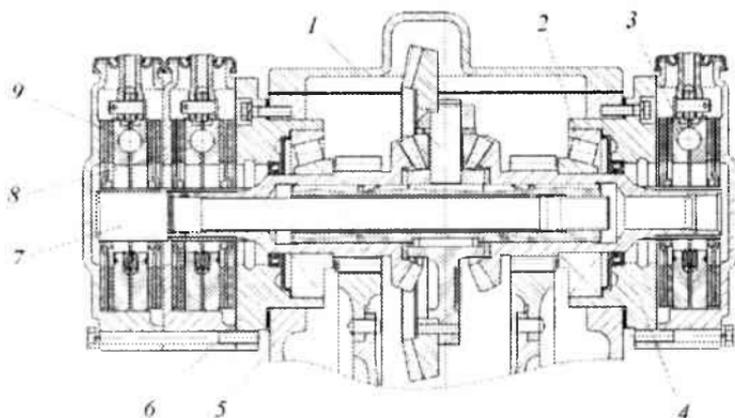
Тормоз стояночный: 1 – дифференциал; 2 – подшипник; 3 – тормоз правый; 4 – корпус правый; 5 – корпус трансмиссии; 6 – корпус левый; 7 – вал стояночного тормоза; 8 – тормоз левый; 9 – тормоз стояночный
